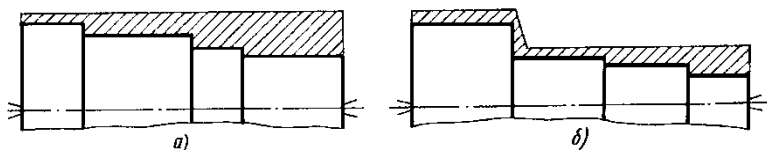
Виды заготовок для ступенчатых валов:
